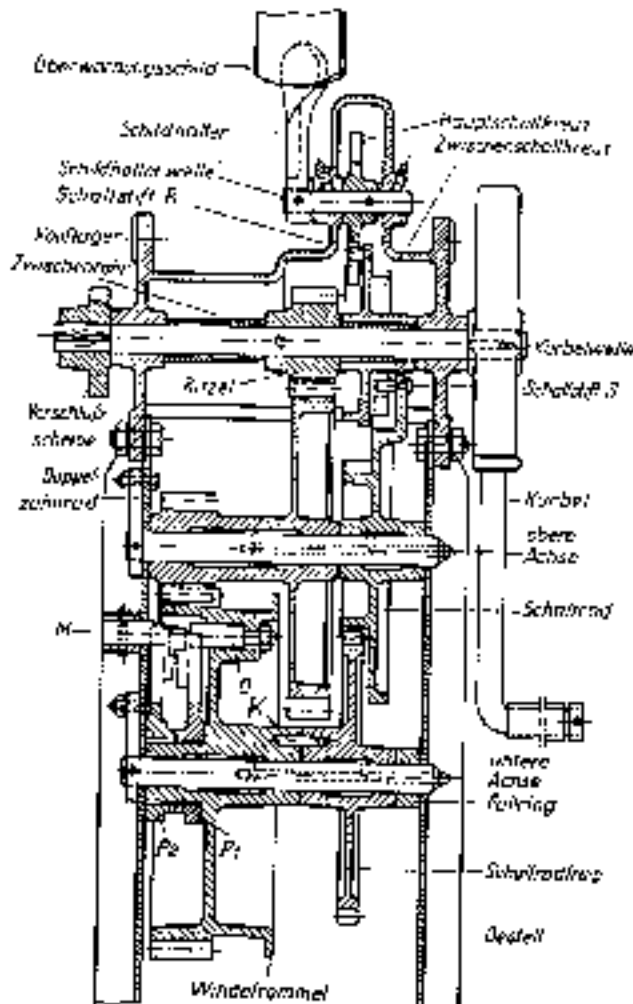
Schnitt durch die Winde für zuverlassbare Schranken
